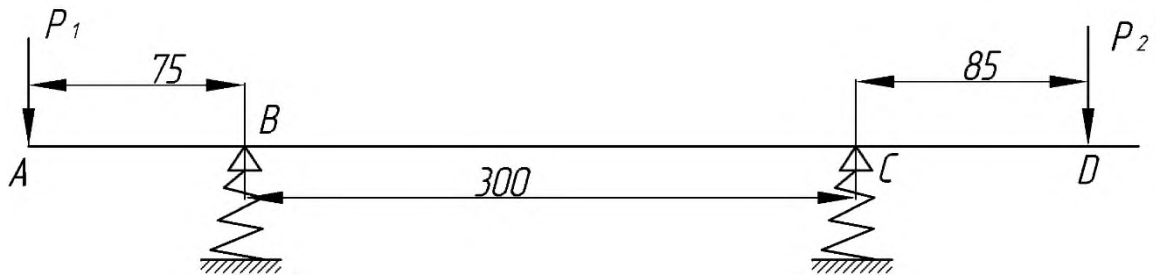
Розрахункова схема шпиндельного вузла
